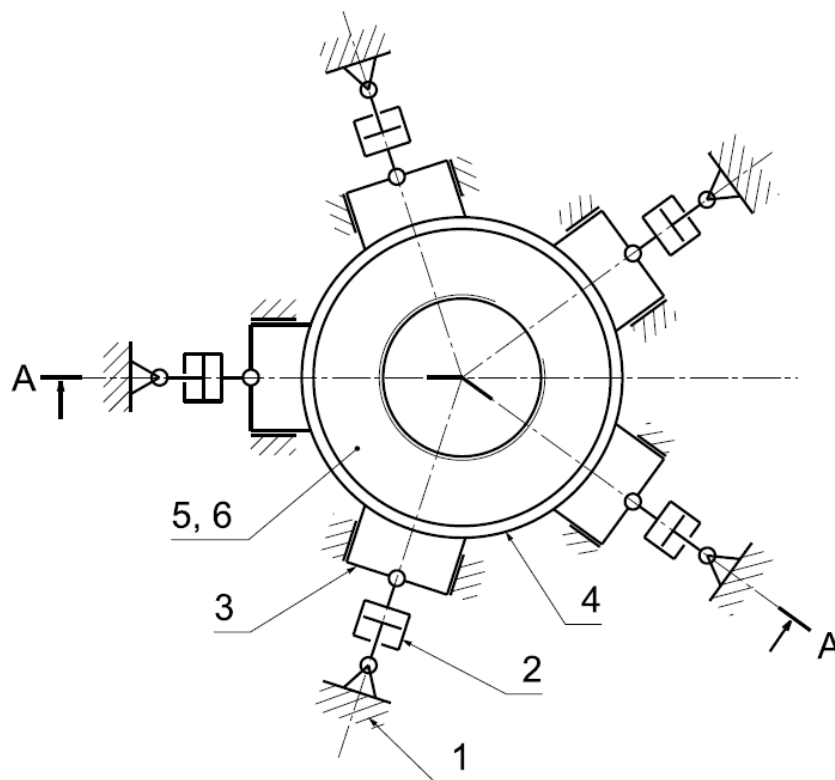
Varianta 1: Minimální zástavbový prostor
